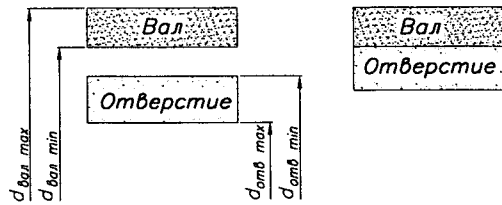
Расположение полей допусков отверстия и вала для посадок с натягом
